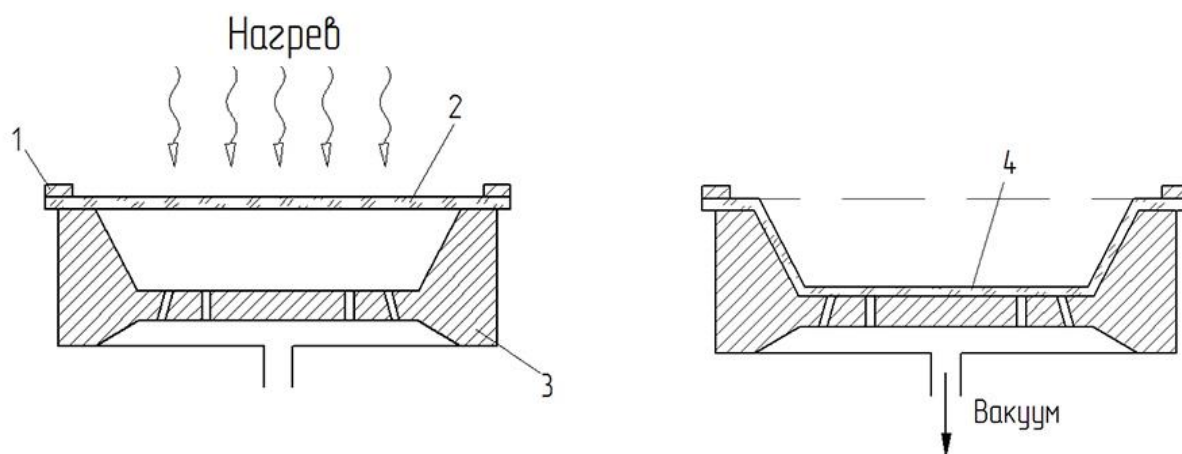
Схема процесса термовакuumного формования термопластов: 1 – зажим; 2 – лист термопласта; 3 – пресс-форма; 4 – изделие
